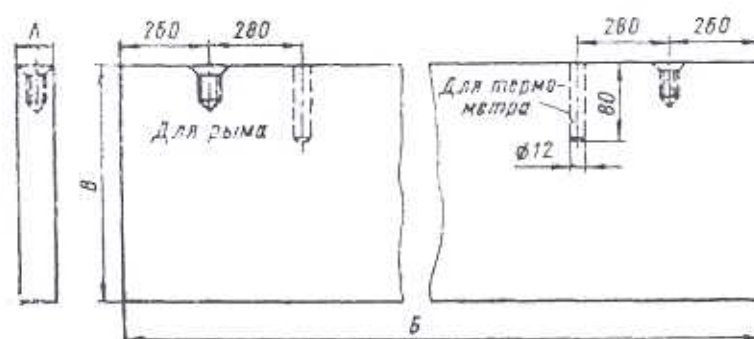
Пресс-планки для опрессовки пазовой части обмотки ротора
